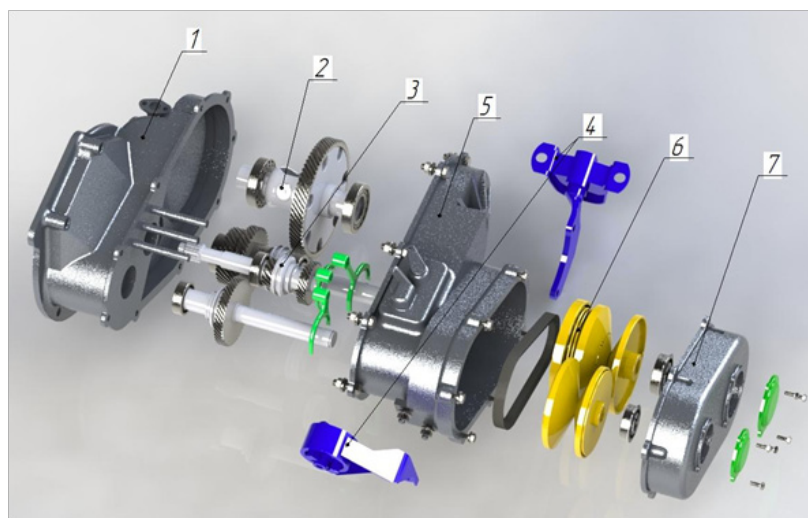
Конструкция коробки передач: 1 – крышка коробки передач; 2 – цилиндрическая главная передача; 3 – механизм реверса вращения; 4 – кронштейны крепления к кузову автомобиля; 5 – корпус вариатора; 6 – клиноременная передача; 7 – крышка клиноременной передачи
